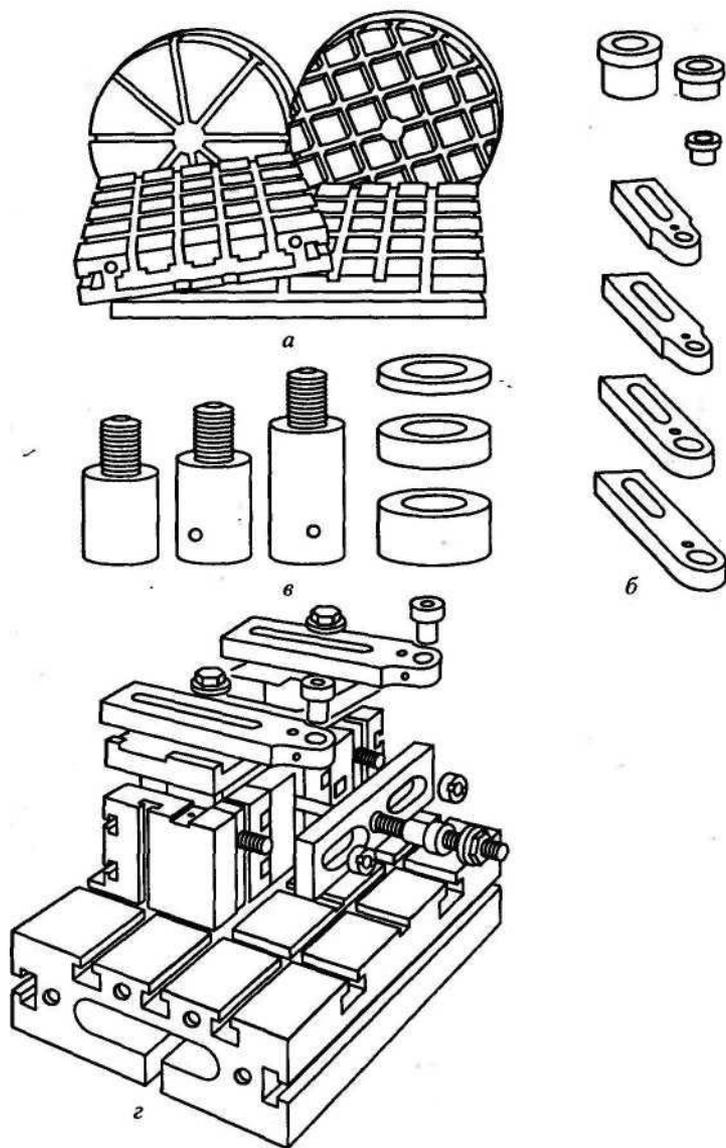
Комплект универсально-сборных приспособлений: а - базовые детали; б - направляющие элементы; в - установочные элементы; г - приспособление в сборе
